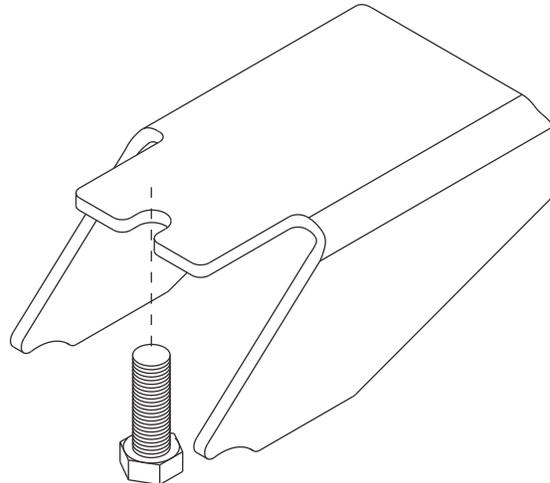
Extensiones de la viga trasera para modelos HC190T/HC230 (solamente kit SURELOK SLKQ)
